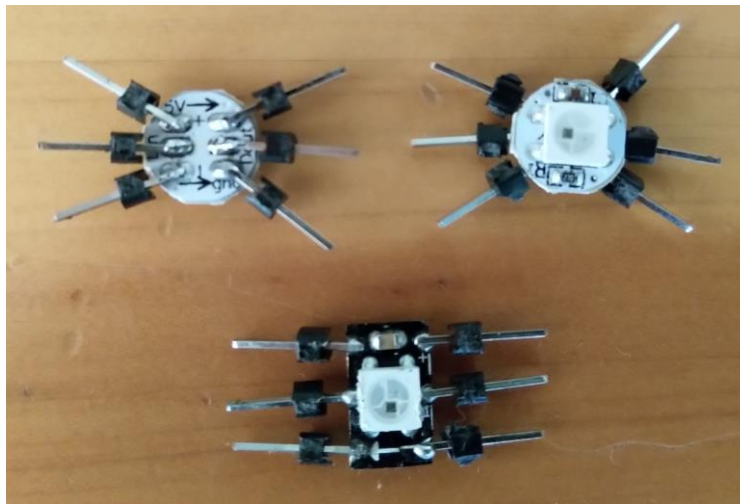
Luces WS2812b con pines soldados a las conexiones
